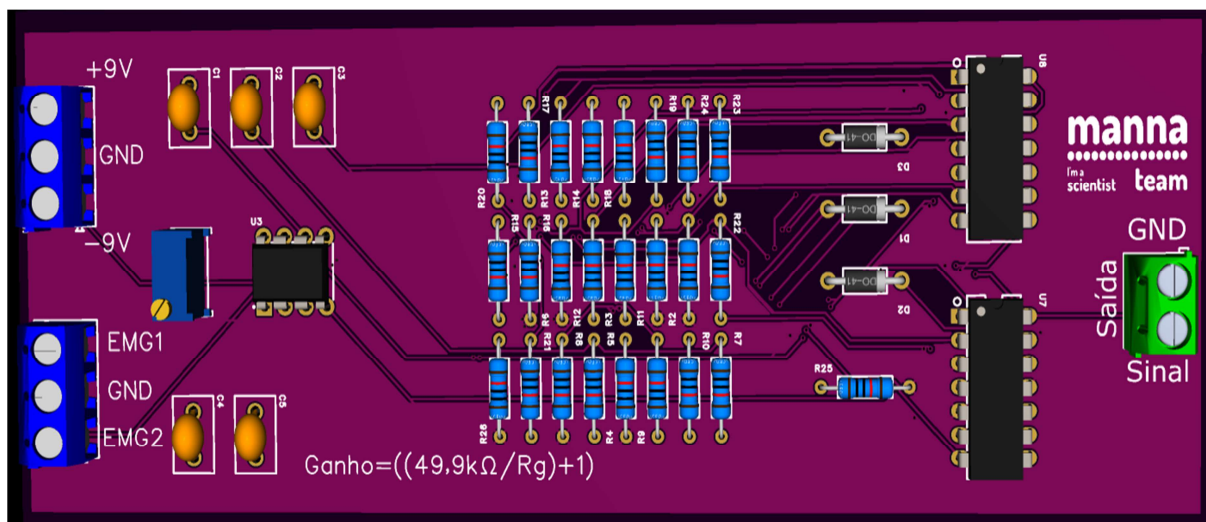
Design Final da PCB do Manna Mio!(Fonte: Autor, 2025)
